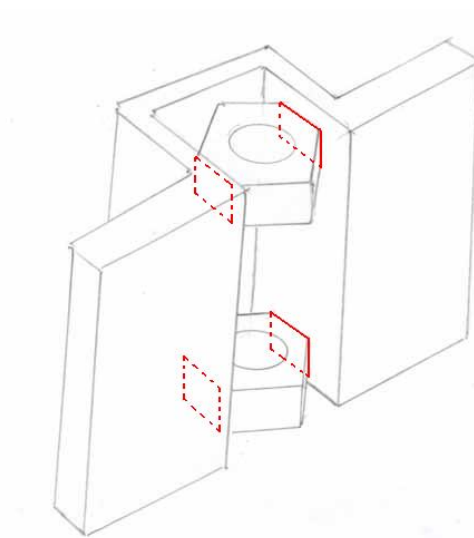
Vista de la soldadura en las tuercas de la guía del husillo
